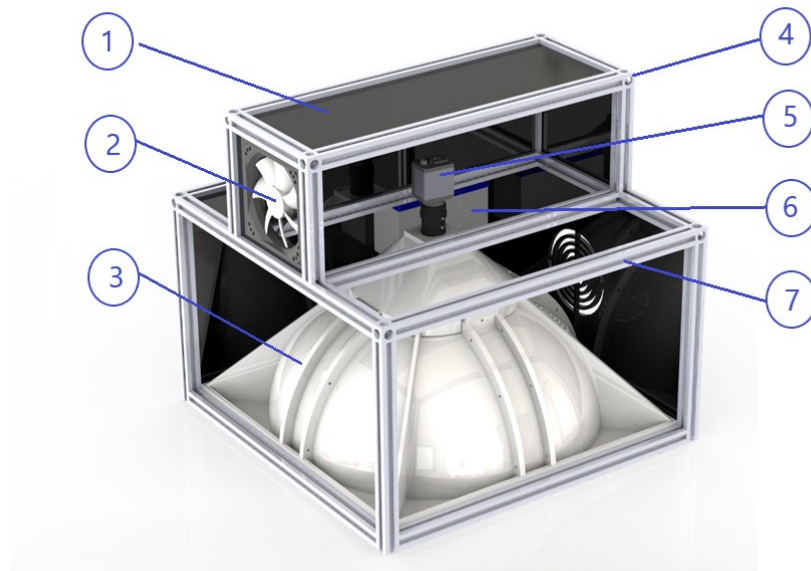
Ensamblaje del SPOCC con perfiles de aluminio mostrando el interior de la estructura. (1) Cubierta plástica para aislar el sistema de la luz exterior, (2) Ventiladores para refrigerar sistema de captura y procesamiento. (3) Luminaria tipo domo. (4) *Cornerblock* utilizado para unir estructura de aluminio. (5) Cámara y óptica para captura de imágenes. (6) Batería para suministrar energía al sistema portátil. (7) Estructura de aluminio
